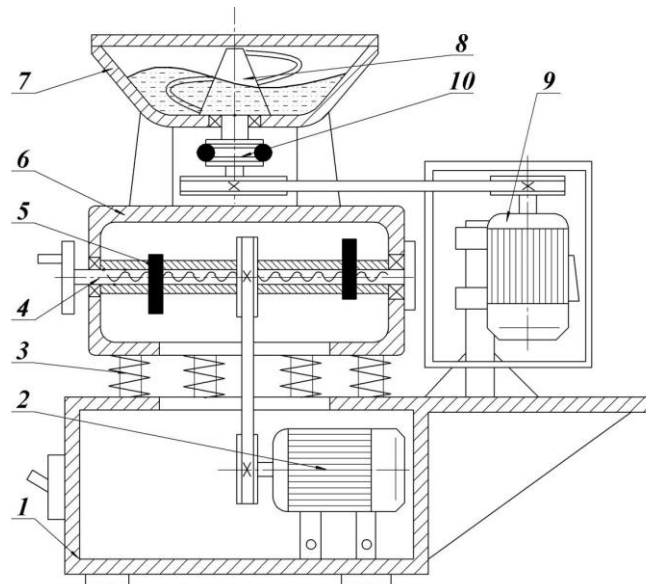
Принципова схема установки для віброабразивної обробки з вертикальним положенням активного робочого органу
